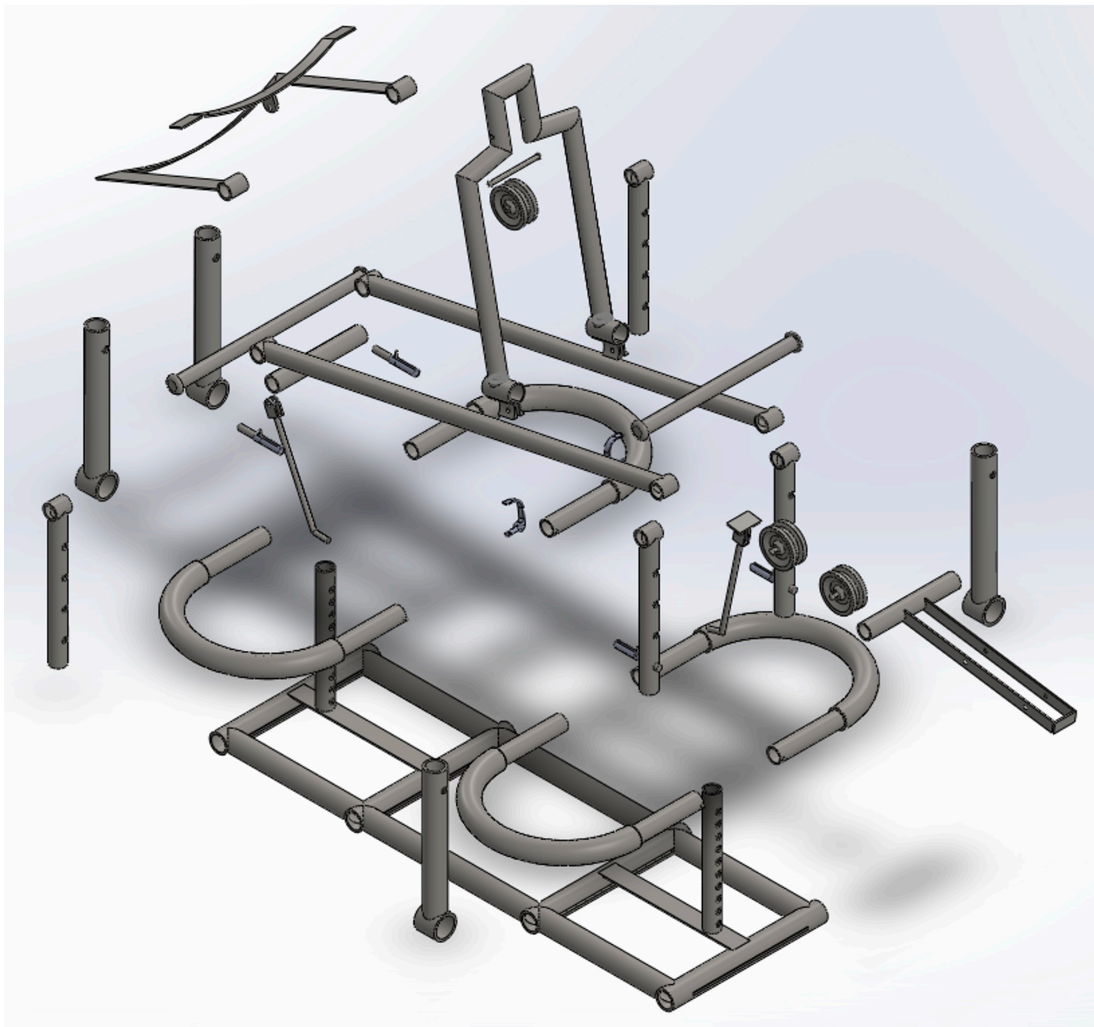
Vista isométrica en explosión de la férula de tracción.
